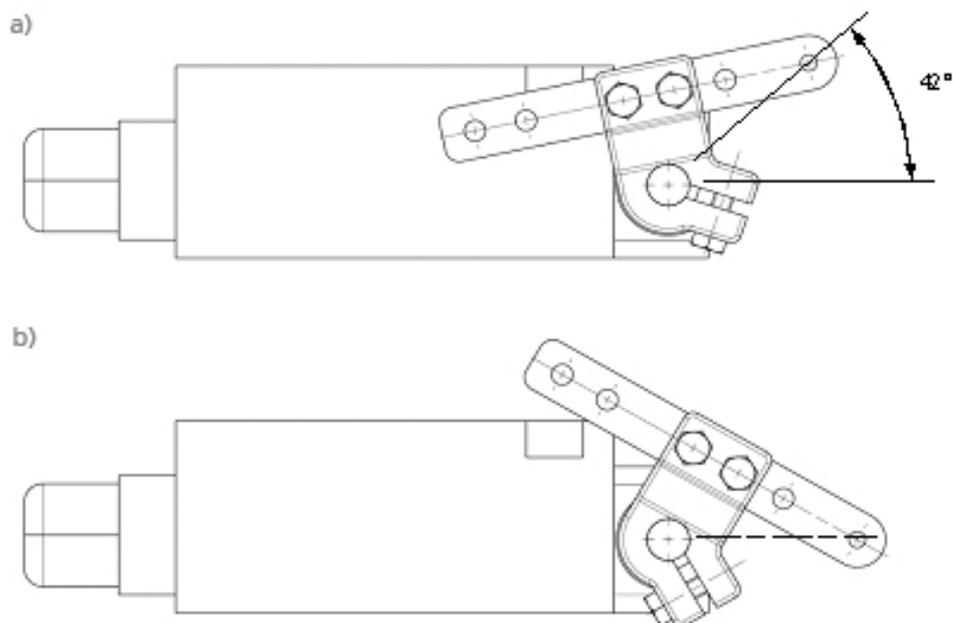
Поплавковый выключатель а) монтажное положение б) положение включения
